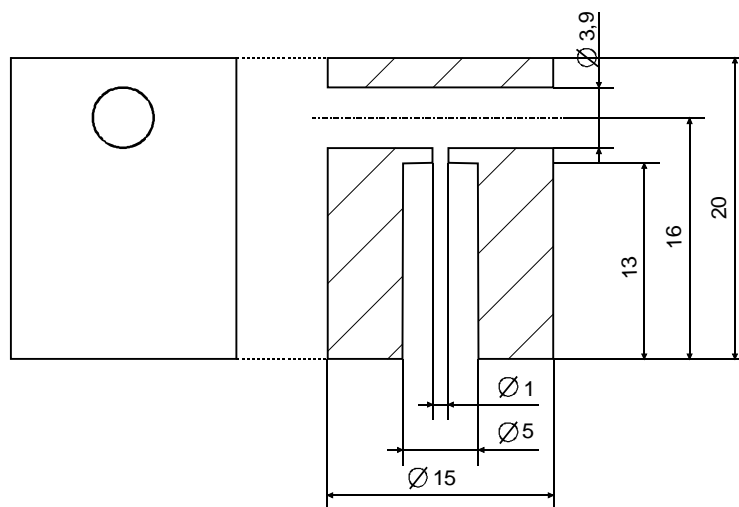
Die Konstruktionszeichnung des Aluminiumblocks, der den Kohlefaserrotor hält
